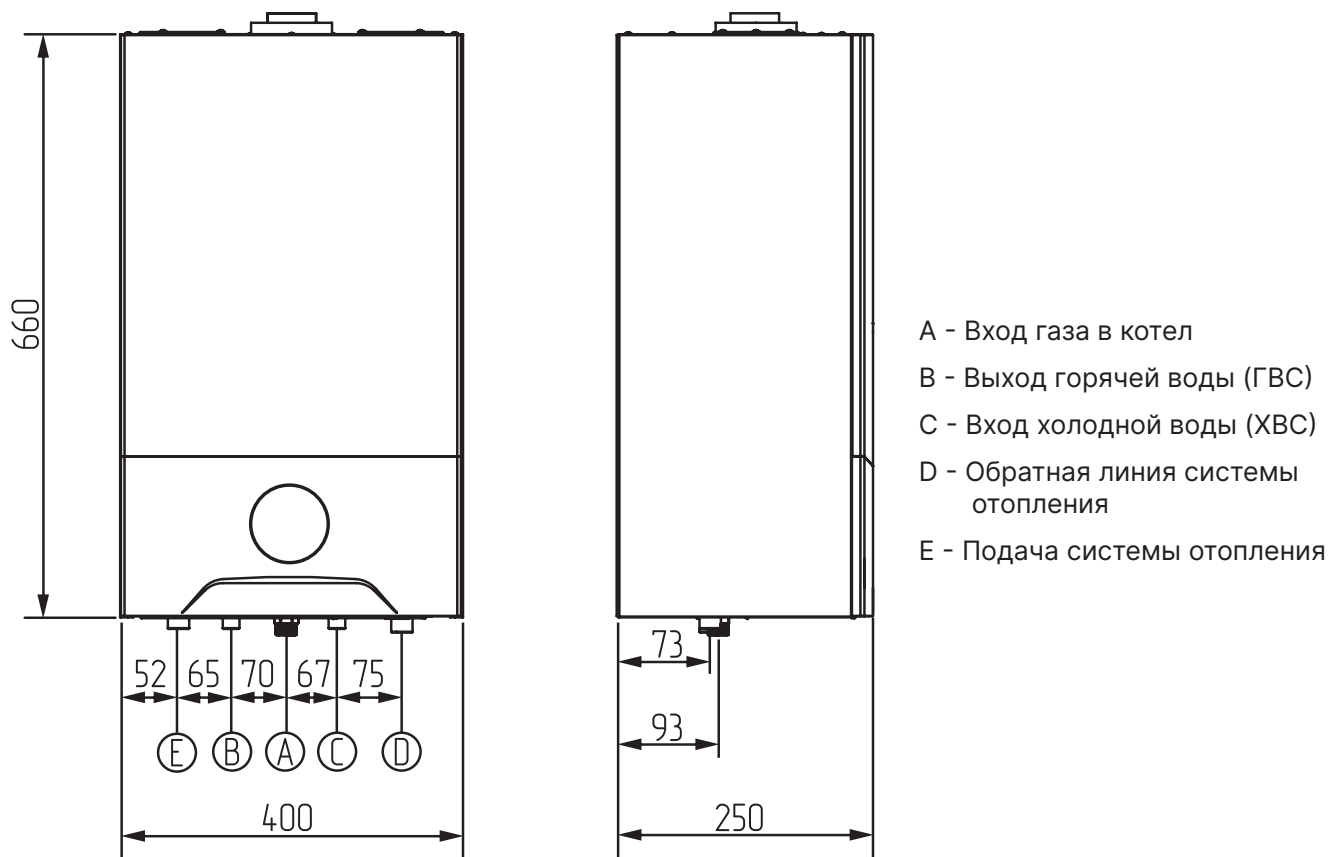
Габаритные размеры и обозначения котла ZOTA ZUMA 18D-24D
